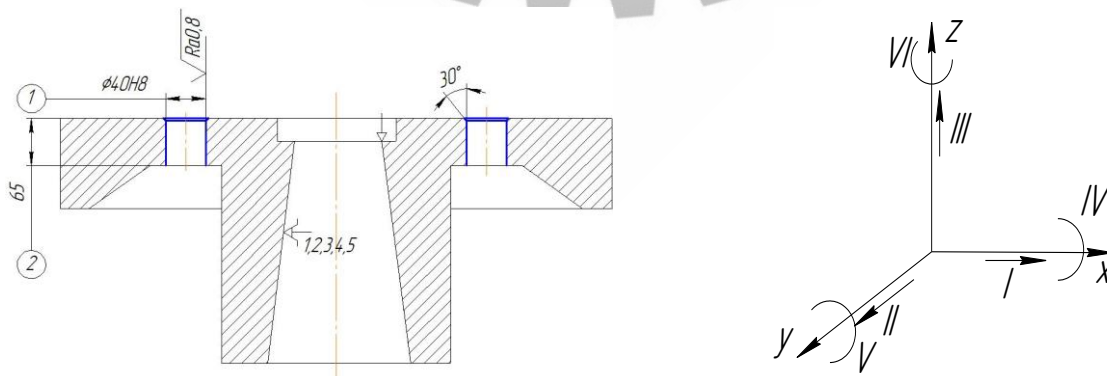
Схема базування заготовки на свердлильну операцію
